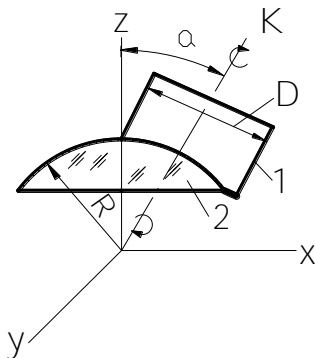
Схема принудительного формообразования сферической поверхности:
